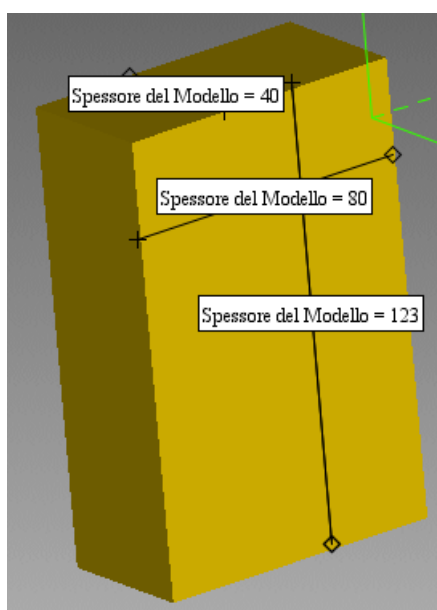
dimensioni del semilavorato 80x123 millimetri con 40 millimetri di spessore.
